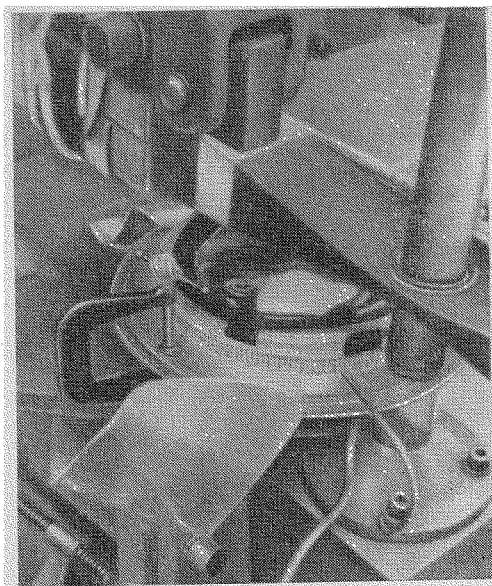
Рабочий момент сварки с помощью колебательной системы типа рис. 22, б
